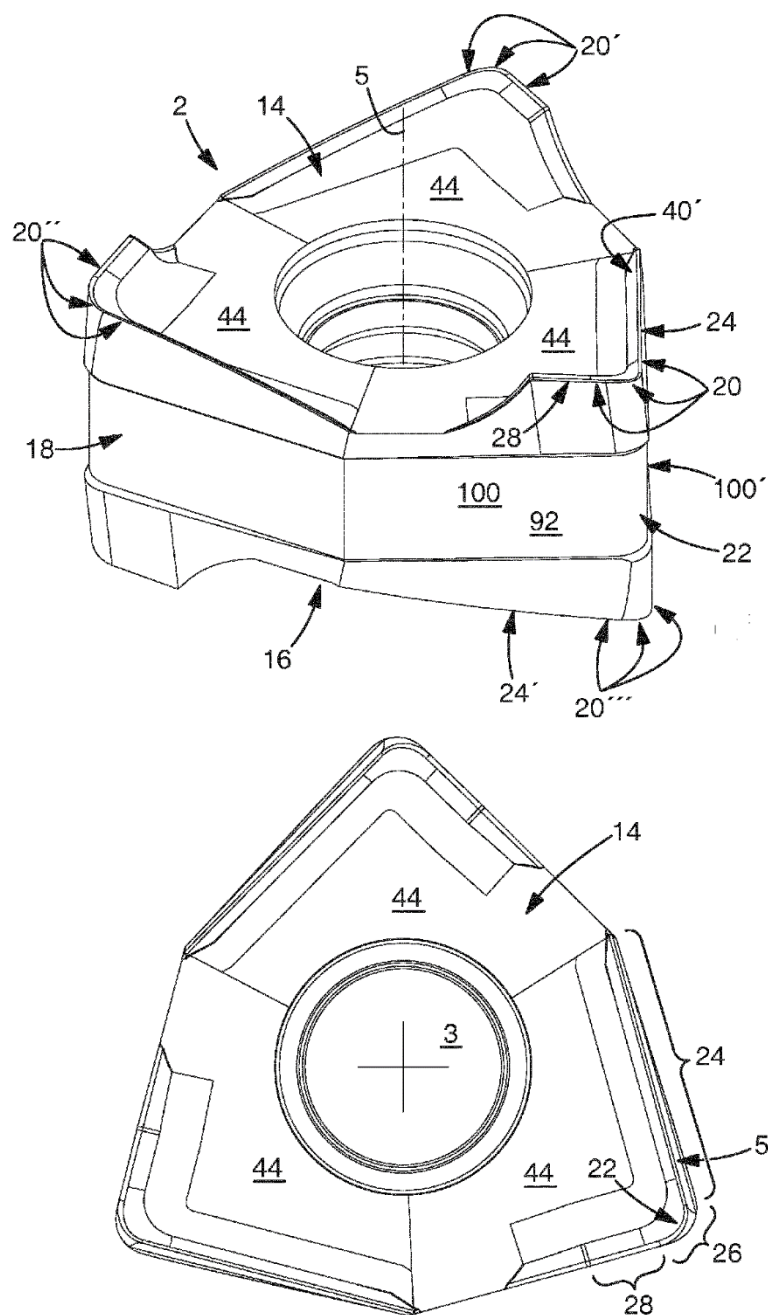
Режущая пластина и инструмент для фрезерования
